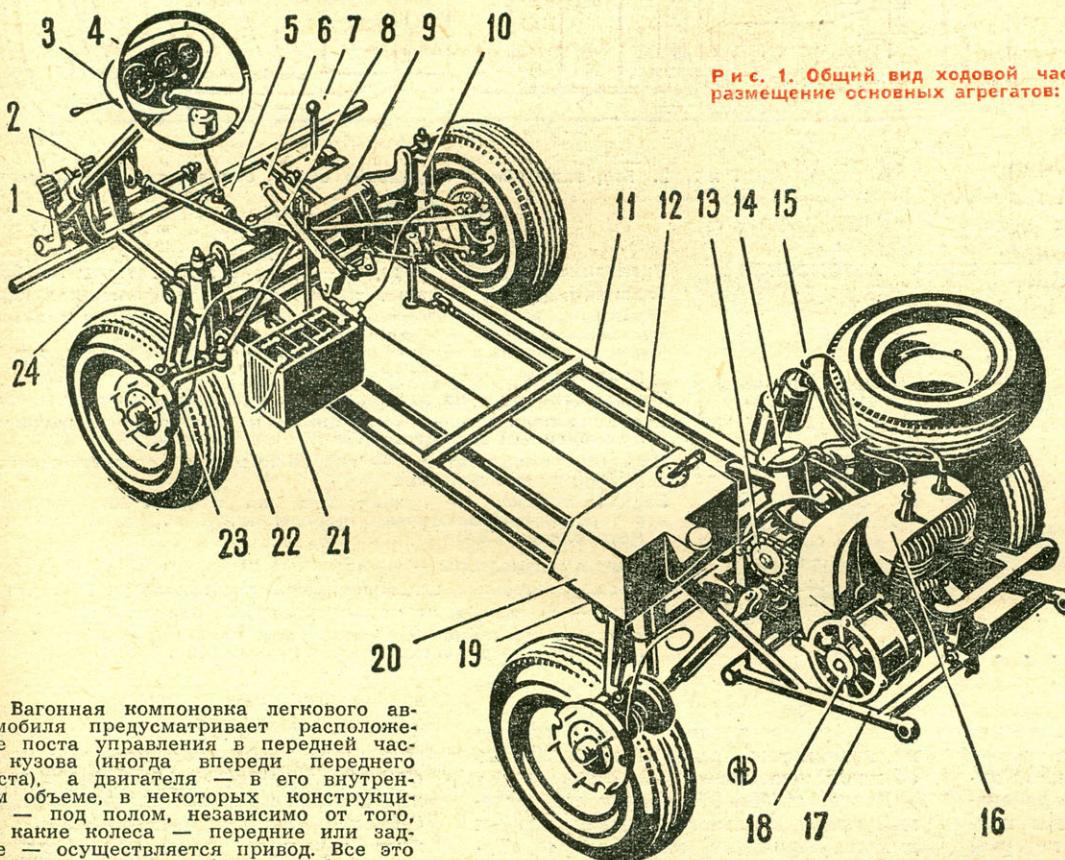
Общий вид ходовой части автомобиля «Муравей» и размещение основных агрегатов:
